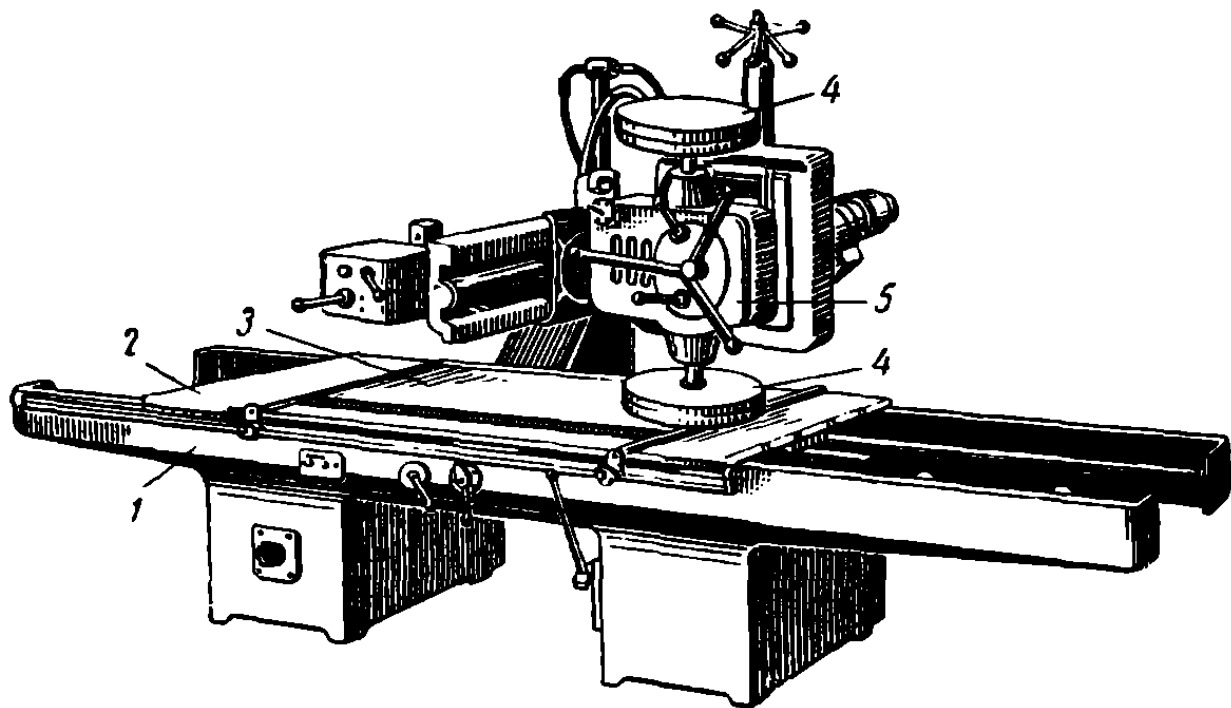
Ротационный плоскополировальный станок марки ГРС
